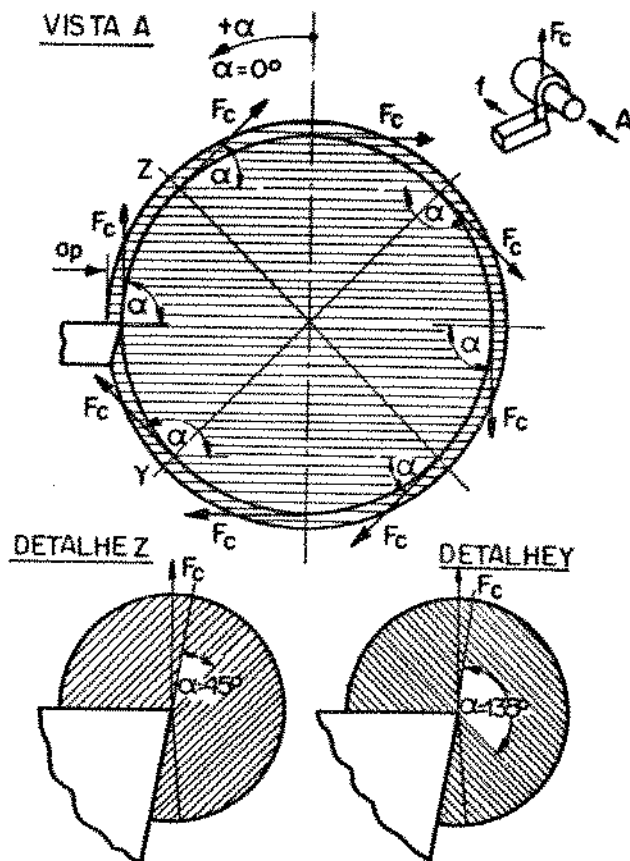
Mecanismo de corte no torneamento de um laminado [18].
